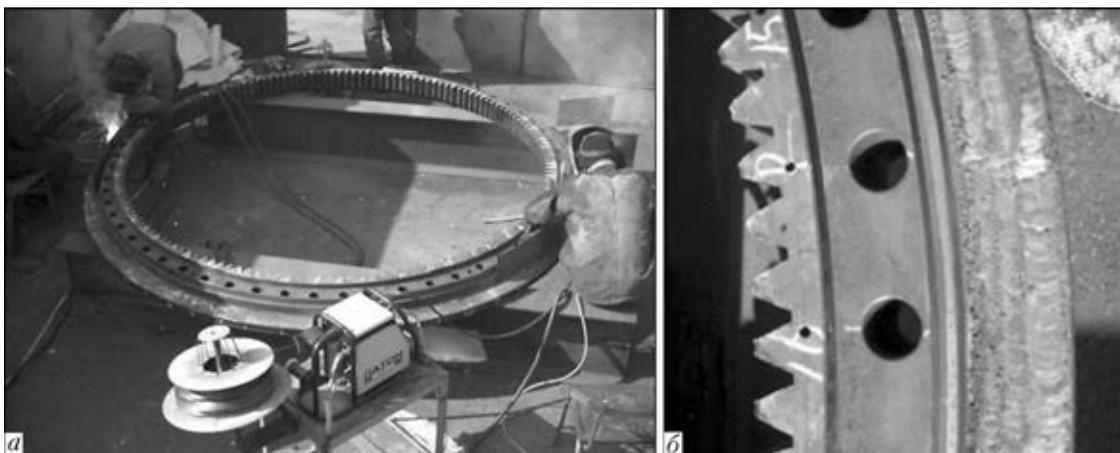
Наплавка зубчатого кольца одновременно двумя наплавщиками (а) и наплавленный участок зубчатого кольца (б)
